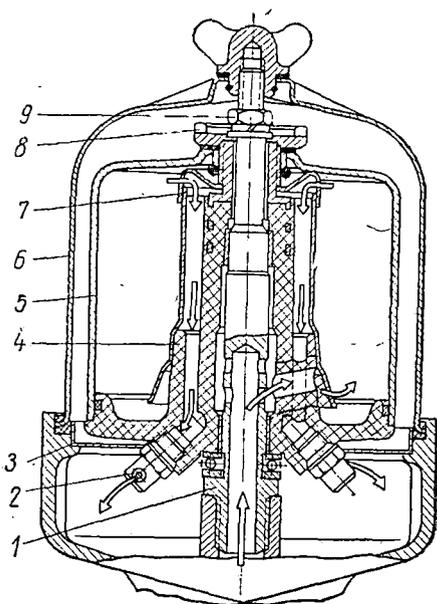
Фильтр центробежной очистки масла двигателя автомобиля ГАЗ-53:
